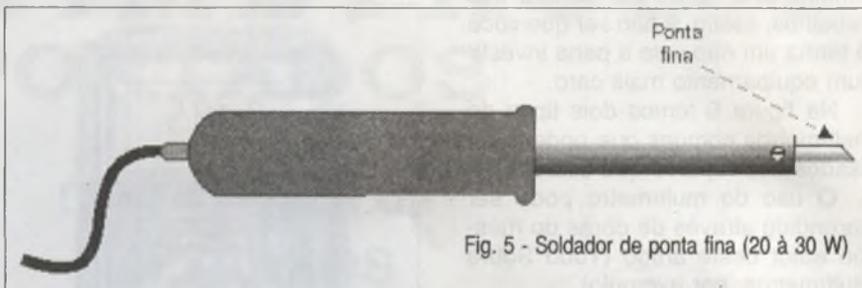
Soldador de ponta fina (20 à 30 W)
